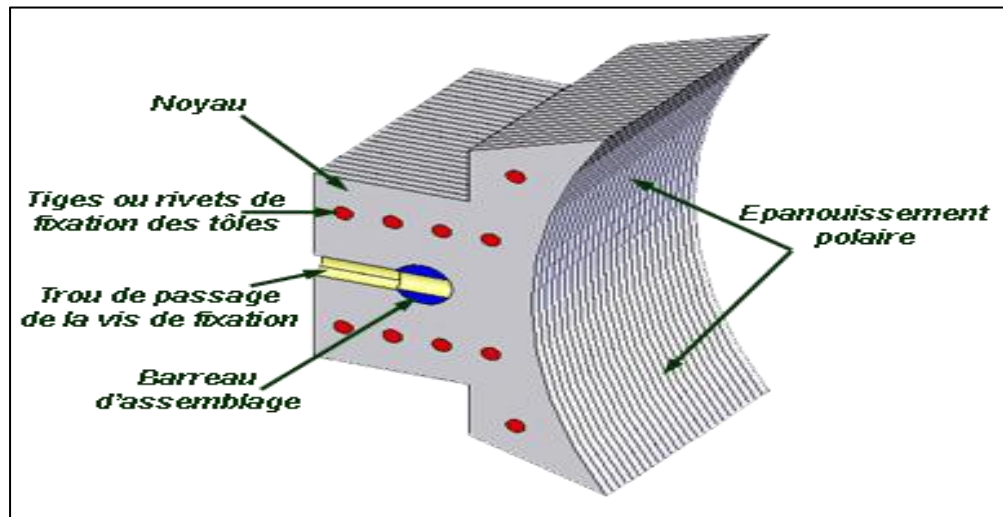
Pôle principal d'une Machine à Courant Continu
